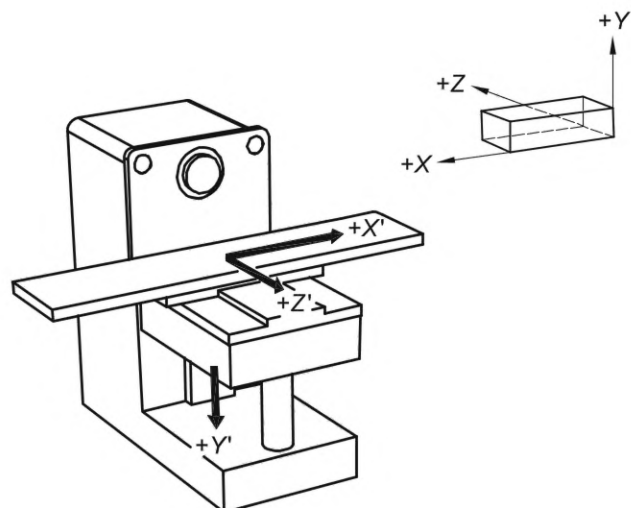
Консольно-фрезерный горизонтальный станок
